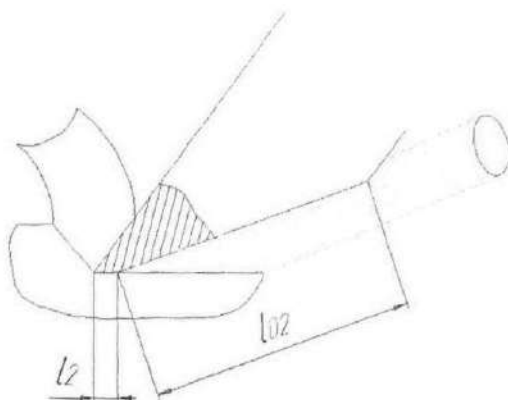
Схема охлаждения режущего инструмента при подаче СОТС на заднюю поверхность режущего клина.
